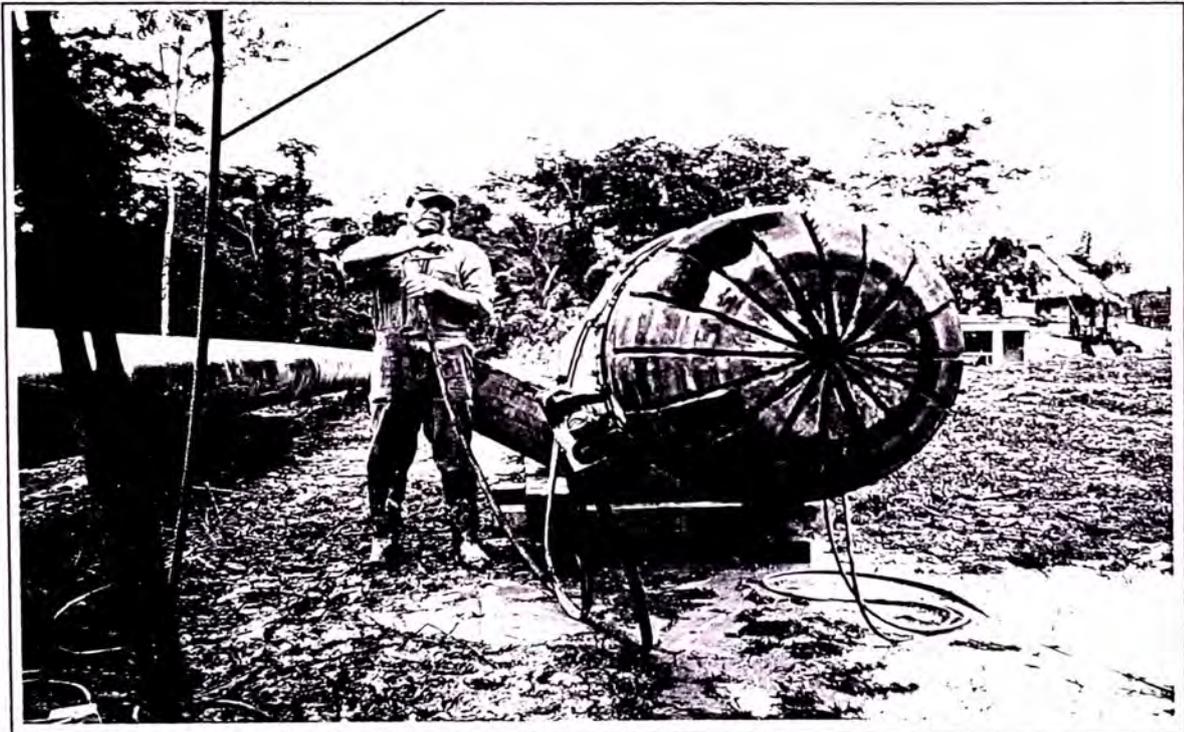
Corte de la sección de tubo empleado para elaborar Cabezal.
